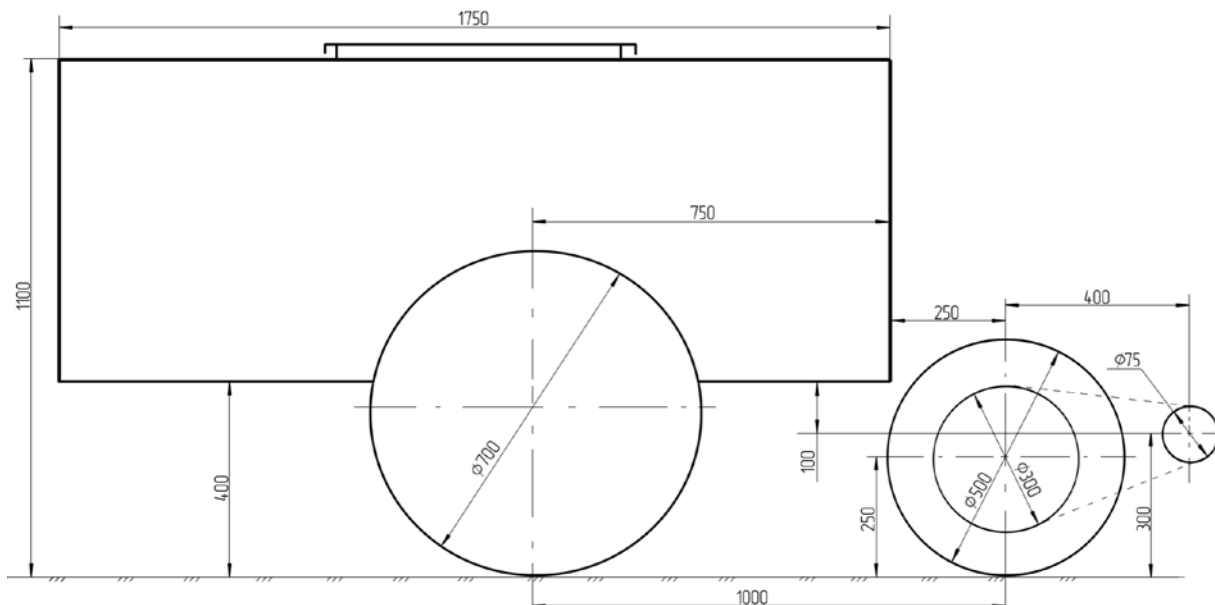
Схема компоновки индивидуального приводного колеса (вид сбоку)
